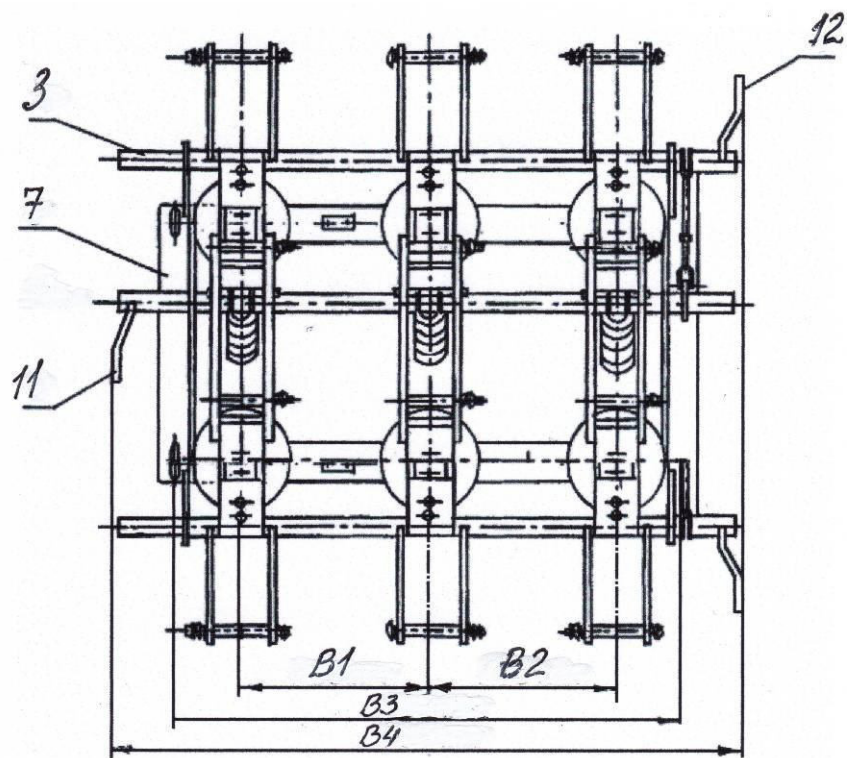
Разъединитель РВЗ – 10 (вид сверху)
